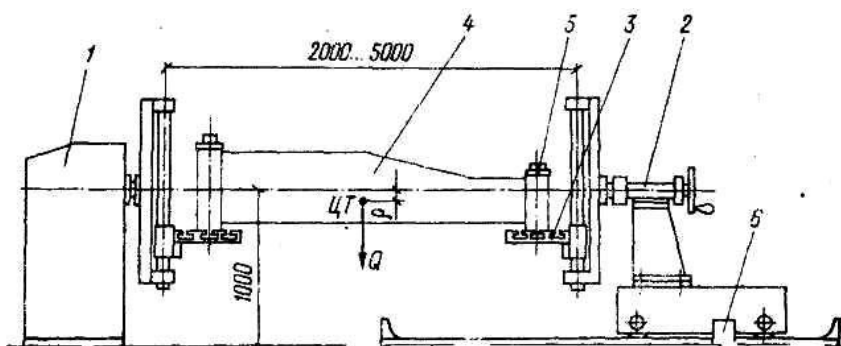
Кантователь двухстоечный: 1 – стойка приводная; 2 – стойка неприводная подвижная; 3 – приспособление крепежное; 4 – изделие; 5 – зажим; 6 – рельсовый захват; CT – центр тяжести вращающихся масс Q , p – эксцентриситет
